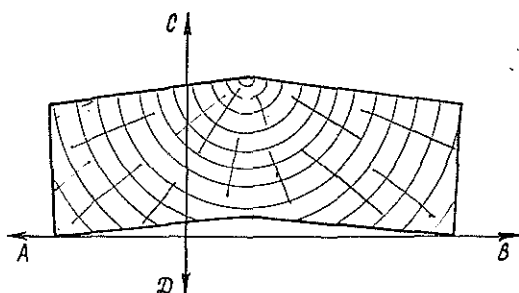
Схема базирования покоробленной доски при получении заготовок.
